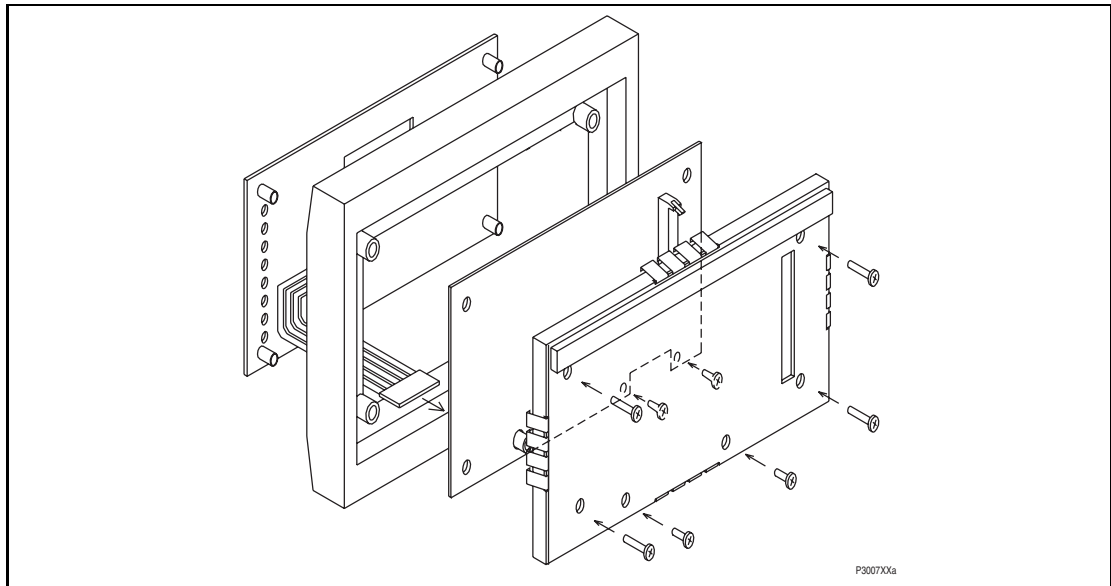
ASSEMBLAGE DE LA FACE AVANT
